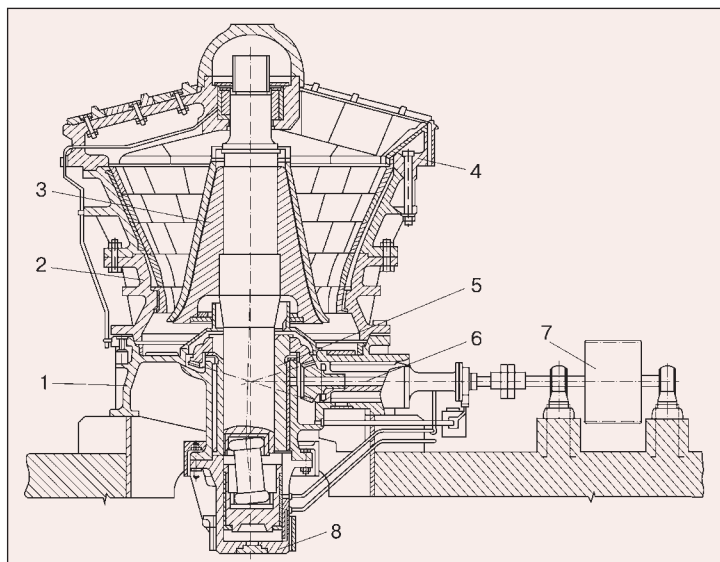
Конусная дробилка ККД 1500/180: 1 — нижняя часть станины; 2 — чаша; 3 — дробящий конус; 4 — траверса; 5 — эксцентрик; 6 — приводной вал; 7 — привод; 8 — крышка
